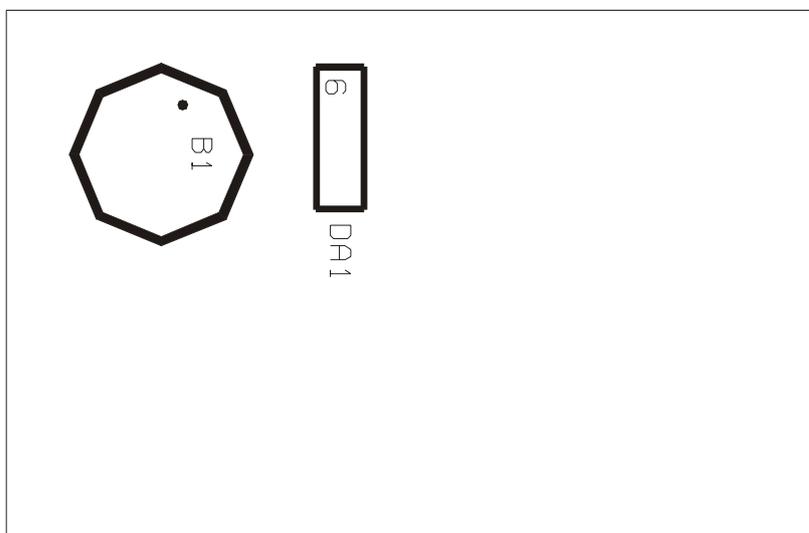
Сборочный чертеж платы блока газоподачи на м/с. TDA1151. Сторона пайки.
